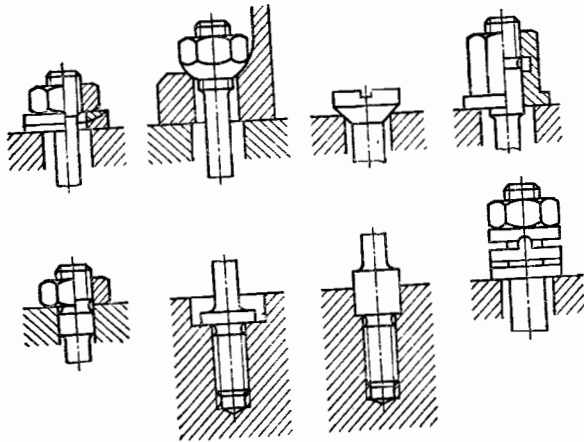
Конструктивные способы разгрузки резьбы от напряжений изгиба
